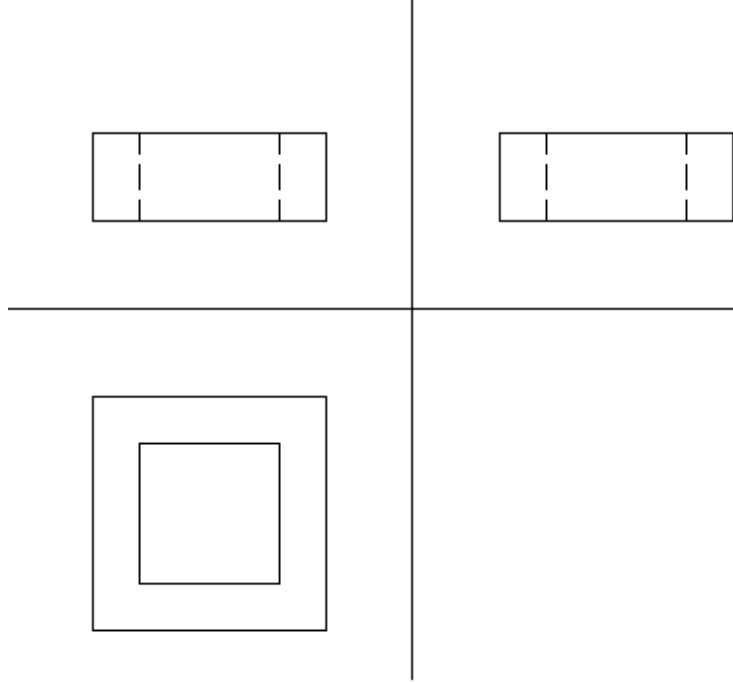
Temel boyutların profil düzlemine taşınması
